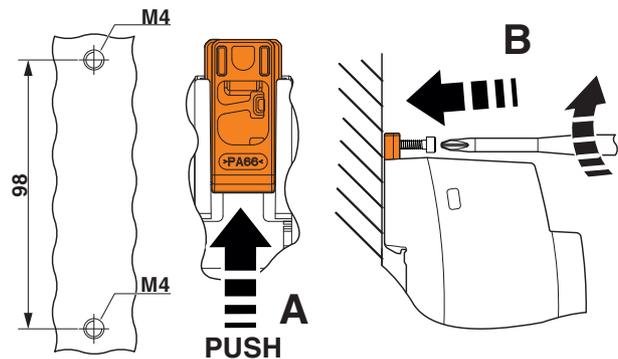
Schraubbefestigung der Stromversorgung auf die Montagefläche
